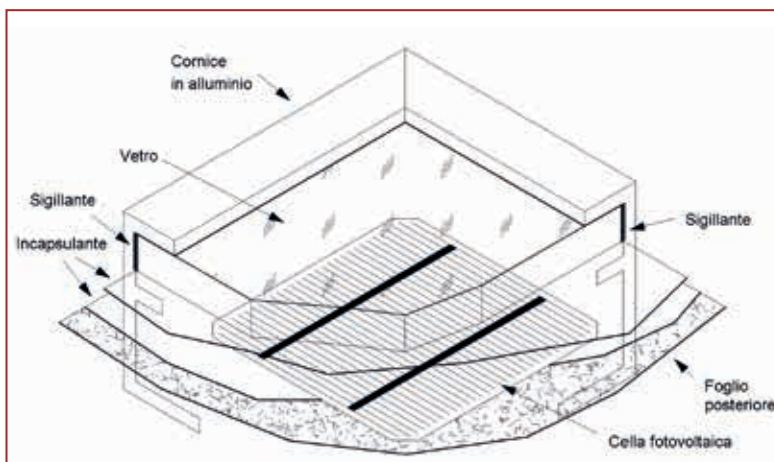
Particolare della vista in sezione di un modulo fotovoltaico.
